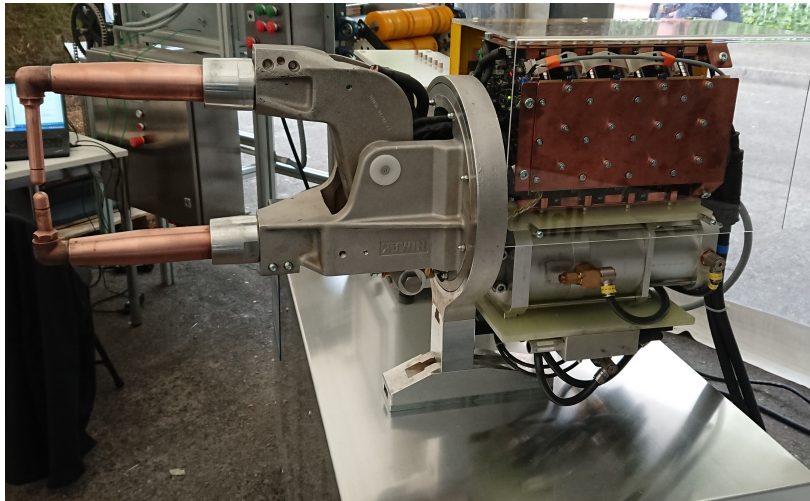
Foto der Handschweißzange und der Gleichspannungswandler.
